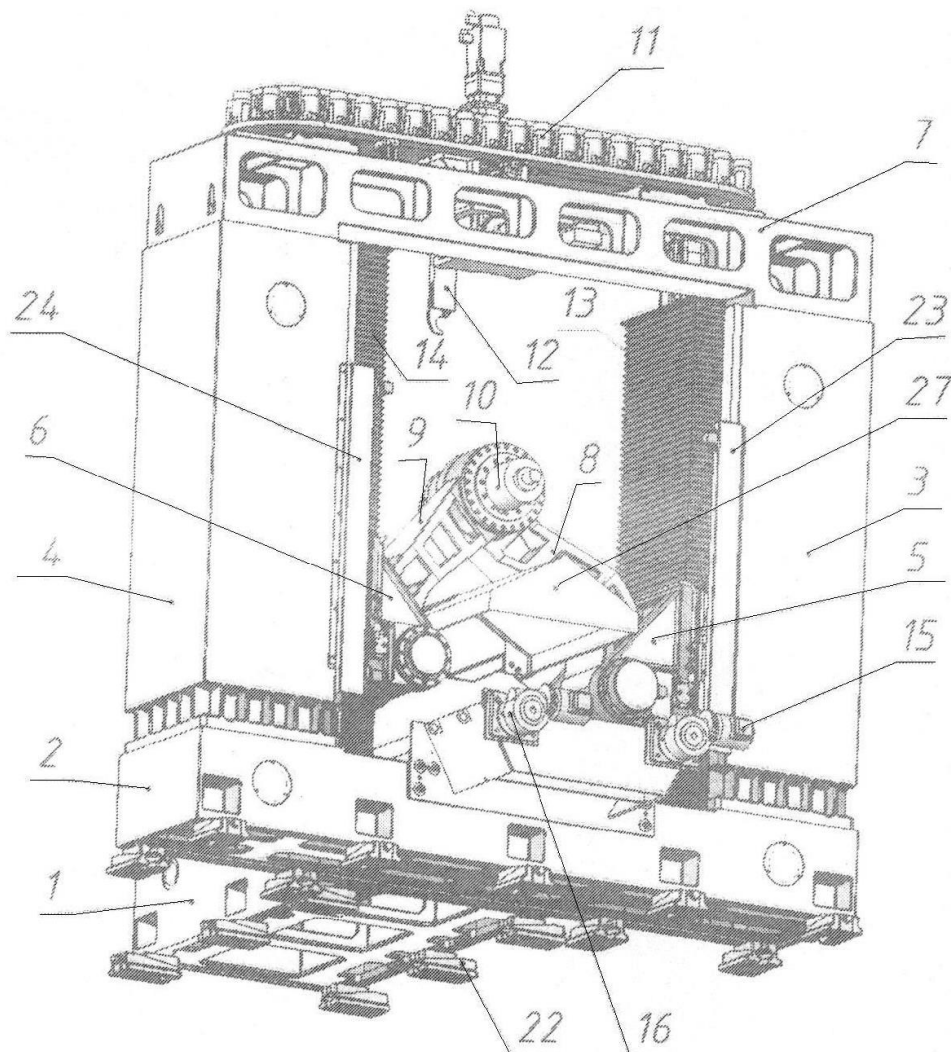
Високошвидкісний обробний центр типу «біпод» з гібридною кінематичною структурою (вигляд ззаду)
